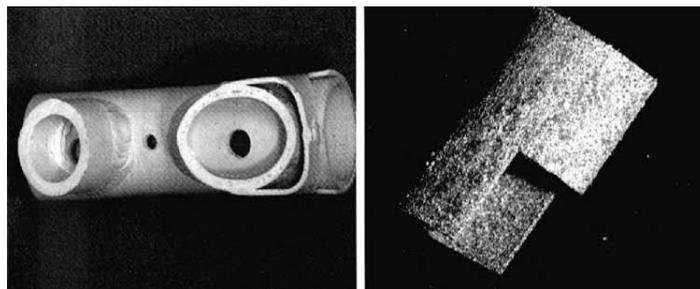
Коррозионные испытания Mg сплава (МДО-модифицированный образец - необработанный образец)
